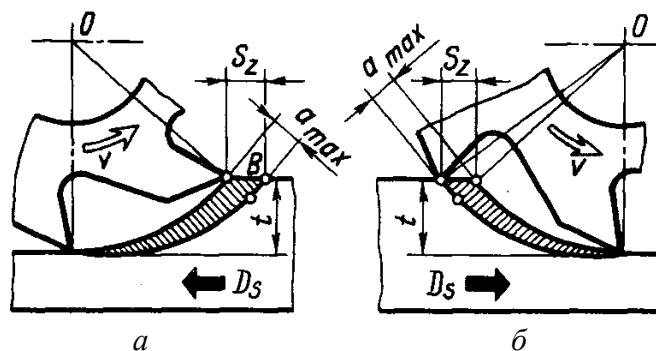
Схемы фрезерования: а – встречное фрезерование; б – попутное
